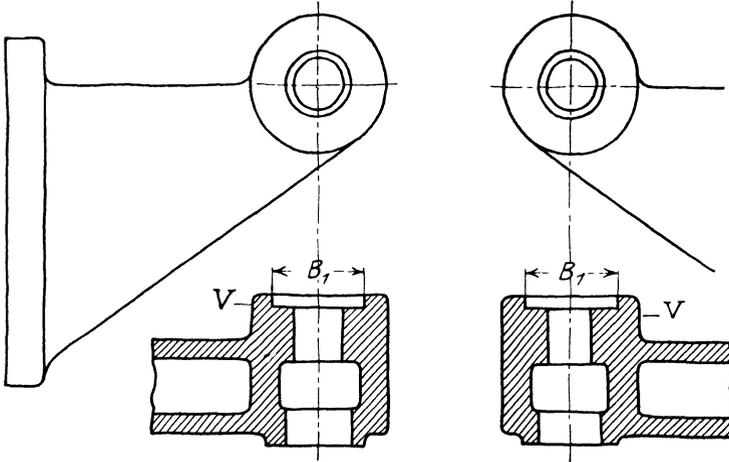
Führungsbock für Links- und Rechtsmaschine.
